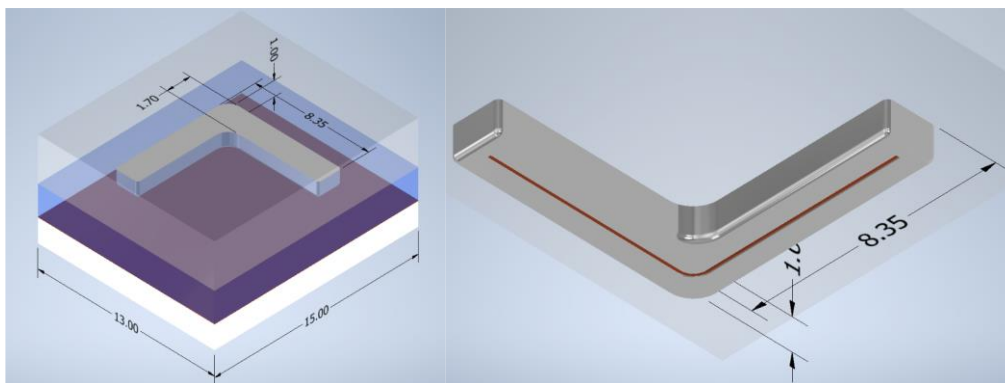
Ensamble del arreglo de materiales para un foco de 15x13 mm y una pista en forma de L, con 1 mm de profundidad (izquierda). El alambre embebido al fondo de la pista, rodeado por el material conductor (derecha).
